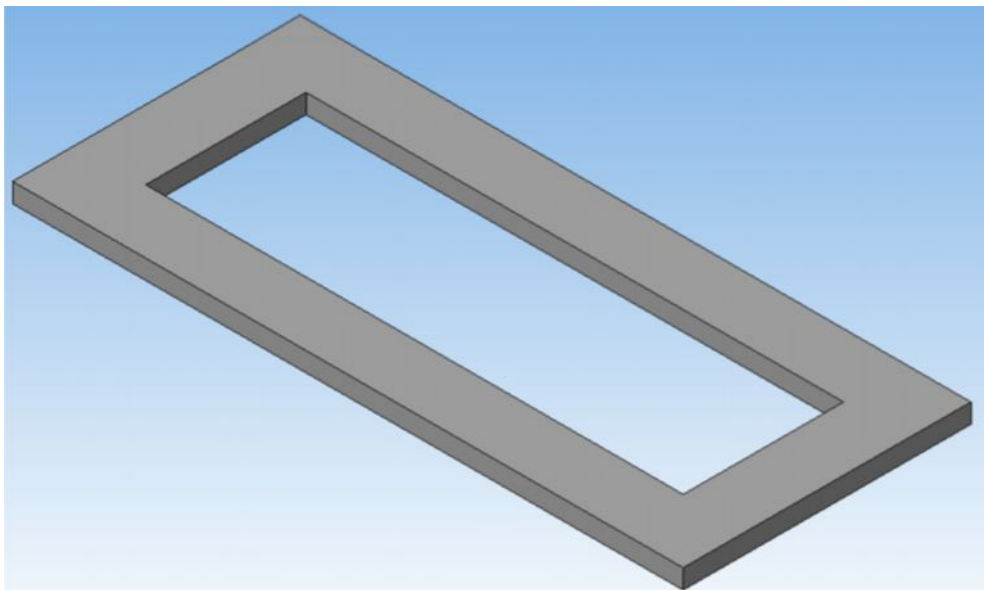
Опорна частина нижньої частини корпусу редуктора
